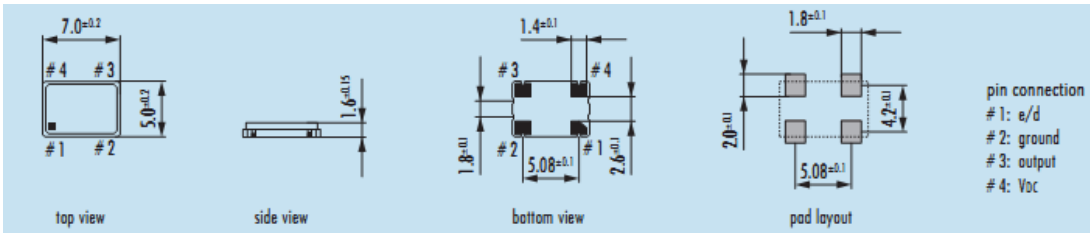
Габарити корпусу O-16.0-VX3E-T1
